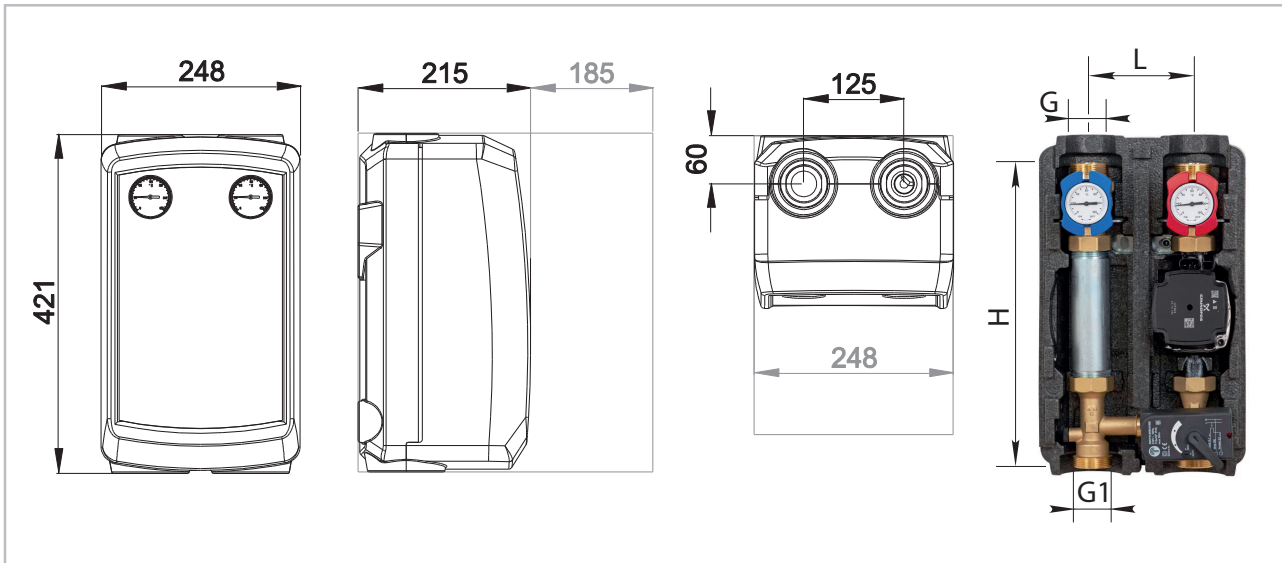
Geräteabmessungen Pumpengruppe HGM (alle Angaben in mm)
